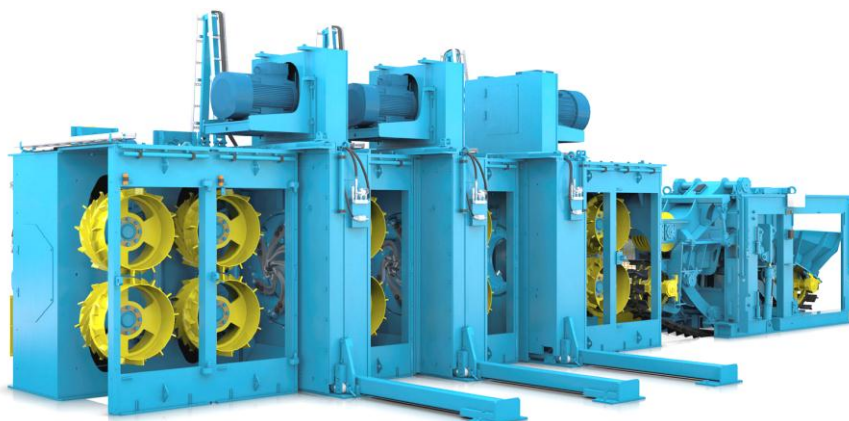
Станок VK8000-Combi-3R с тремя роторными головками
